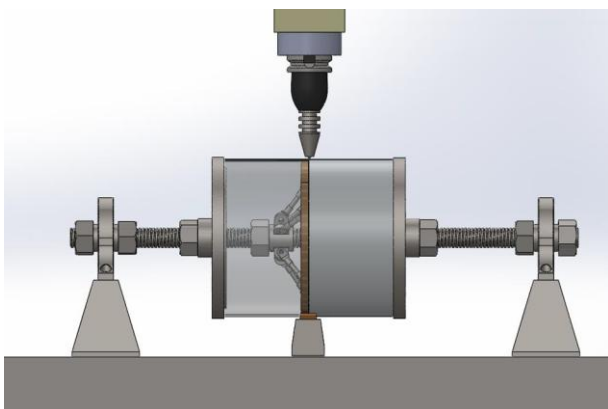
Vista lateral del sistema de soldaduras circunferenciales para la unión de las virolas del cuerpo del tanque.
